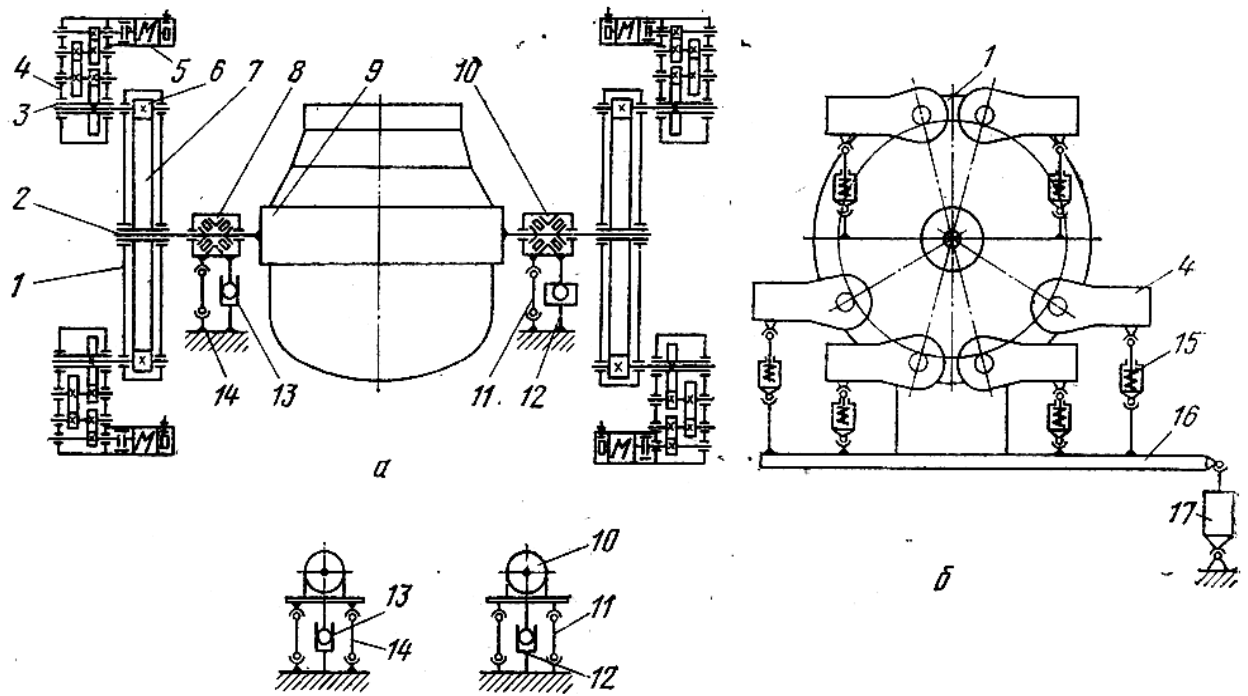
Кинематическая схема двухстороннего навесного механизма поворота КК.
